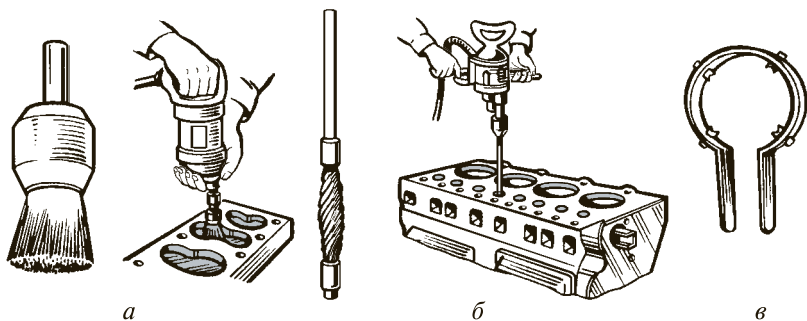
Приспособления для удаления нагара из головки цилиндров [а], из направляющих втулок клапанов [б], из канавки поршней [в]
